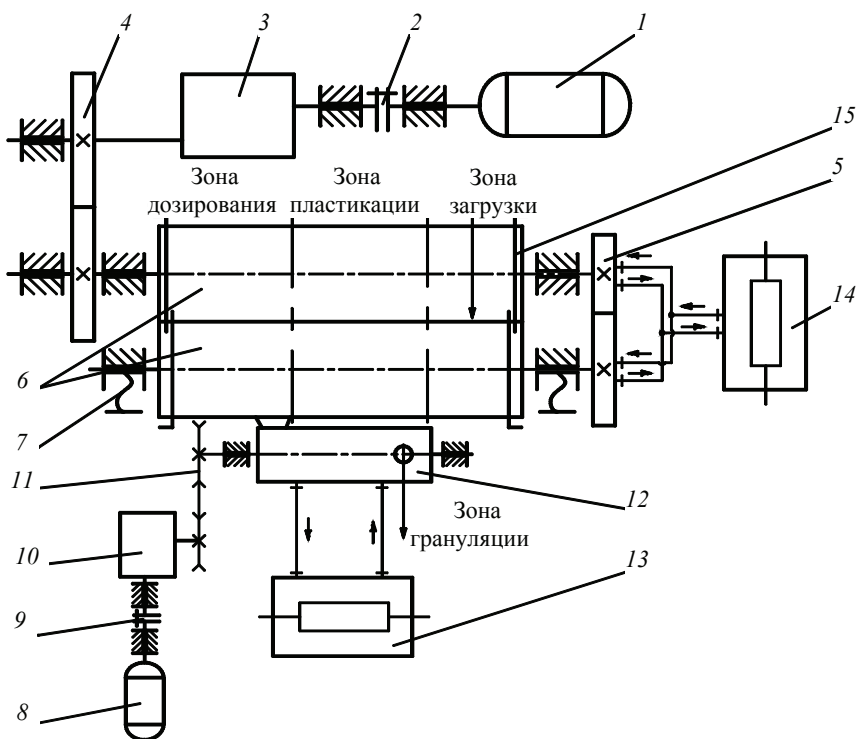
Схема лабораторного валково-шнекового агрегата: 1 – электродвигатель; 2, 9 – муфта; 3 – редуктор; 4 – передаточные шестерни; 5 – фрикционная передача; 6 – валки; 7 – механизм регулировки зазора; 8 – электродвигатель отборочного устройства; 10 – червячный редуктор; 11 – клиноременная передача; 12 – отборочно-шнековое устройство; 13, 14 – термостат; 15 – ограничительные стрелы
